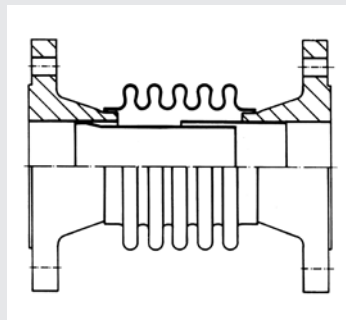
Осевого компенсатор с приварными воротниковыми фланцами
